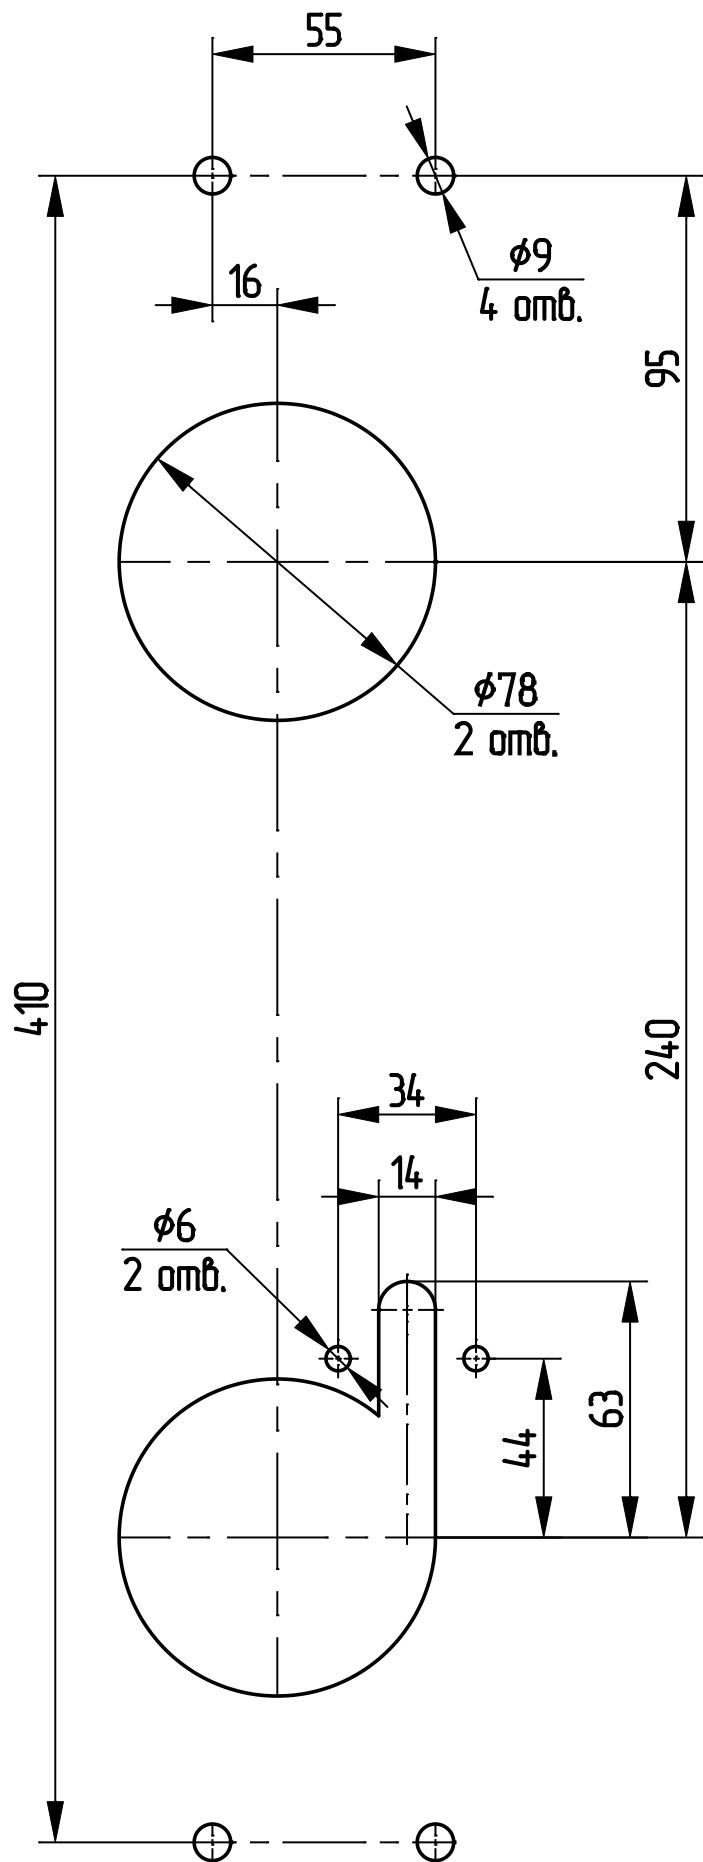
Разметка отверстий для установки приводов ПРК-10Б-25 (вид спереди)
